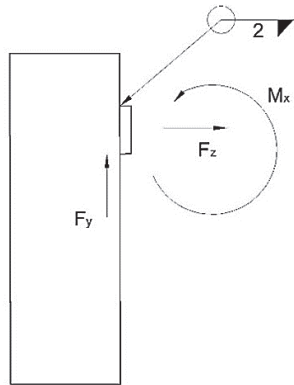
Fuerzas en la junta de soldadura.
